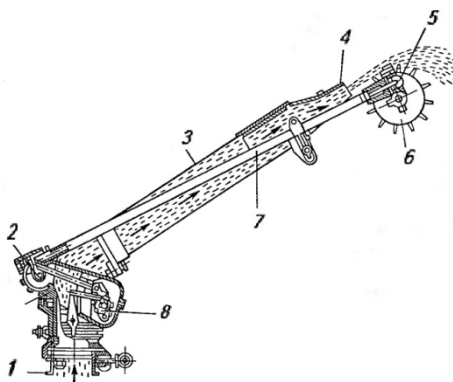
Дальнеструйный дождевательный аппарат: 1 – стакан; 2; 5 – передача; 3 – ствол; 4 – сопло; 6 – турбинка; 7 – вал; 8 – механизм поворота
